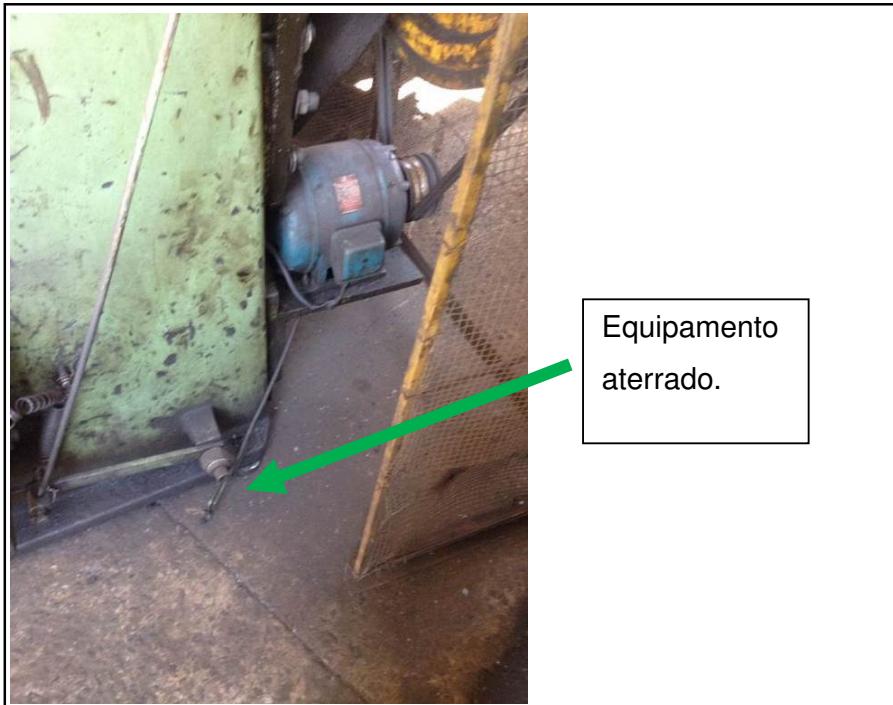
Detalhe da proteção da Rebarbadora 65t
